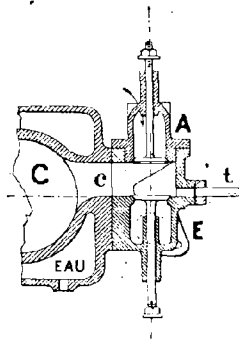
Moteur Daniel Augé. Boîte à soupape.
